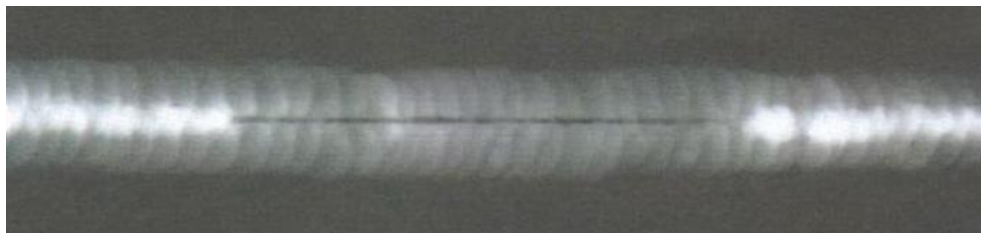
Radiografía de falta de penetración en la soldadura
